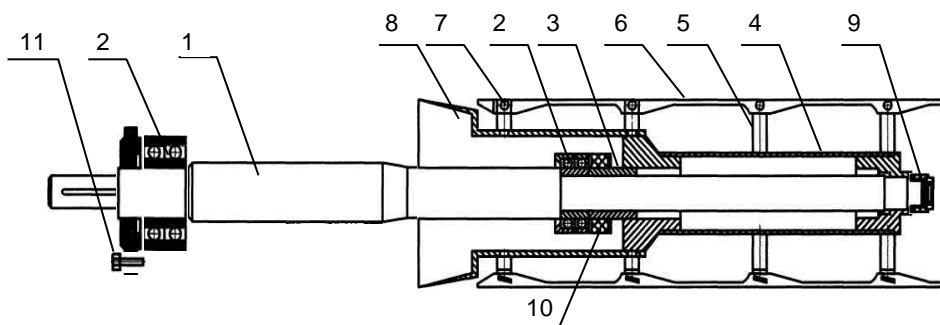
Вал збивача в зборі: 1 – вал; 2 – підшипники; 3 – втулка; 4 – корпус била; 5 – стійка; 6 – лопать била; 7 – кріплення лопаті; 8 – конус; 9 – гайка спеціальна; 10 – ущільнення; 11 – болтове кріплення
